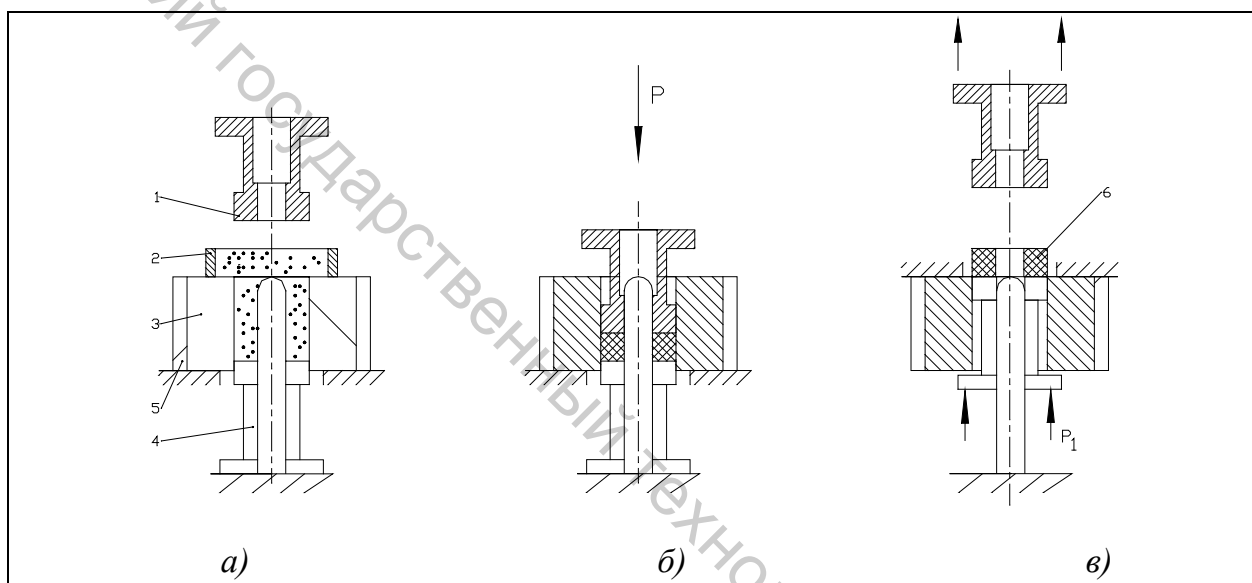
Пресс-форма для одностороннего прессования:
